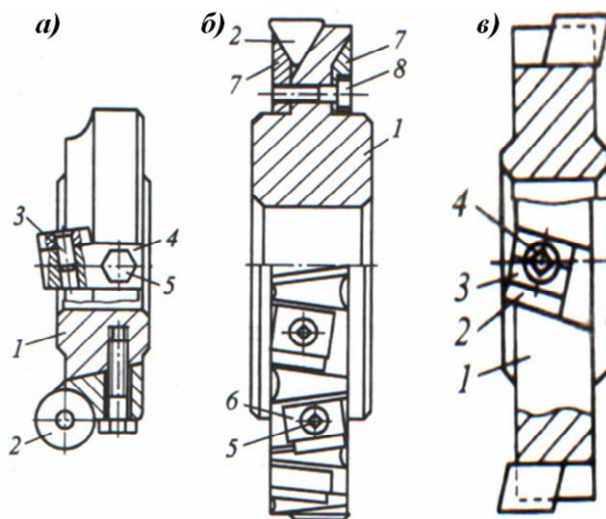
Сборные дисковые фрезы с открытыми базами для крепления СМП
